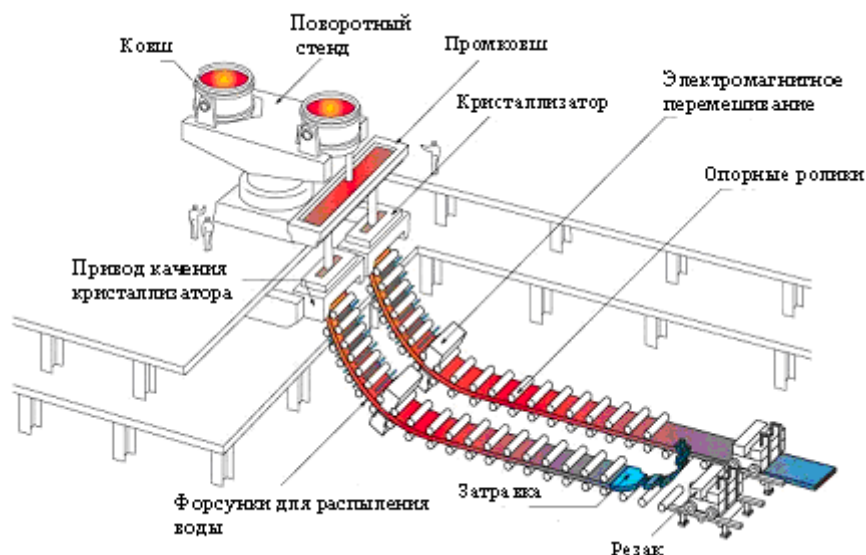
Общая схема разливки стали на МНЛЗ
